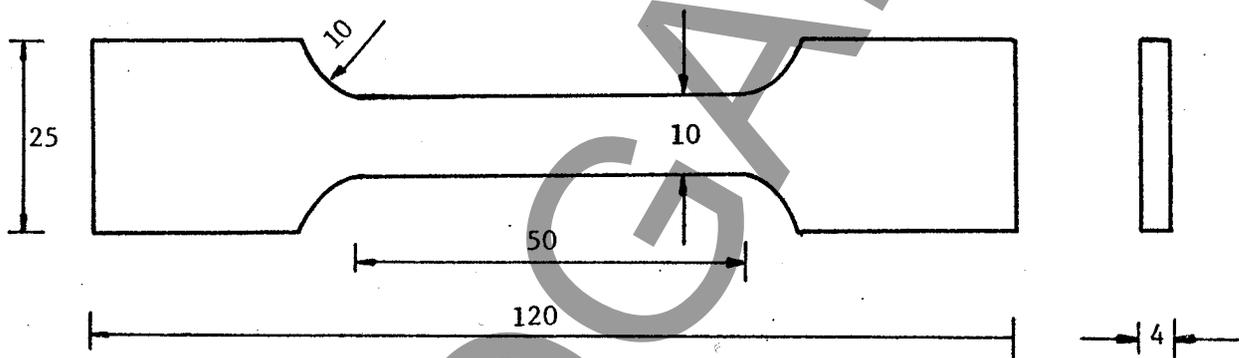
Dimensões do corpo de prova (Dimensões em mm)
